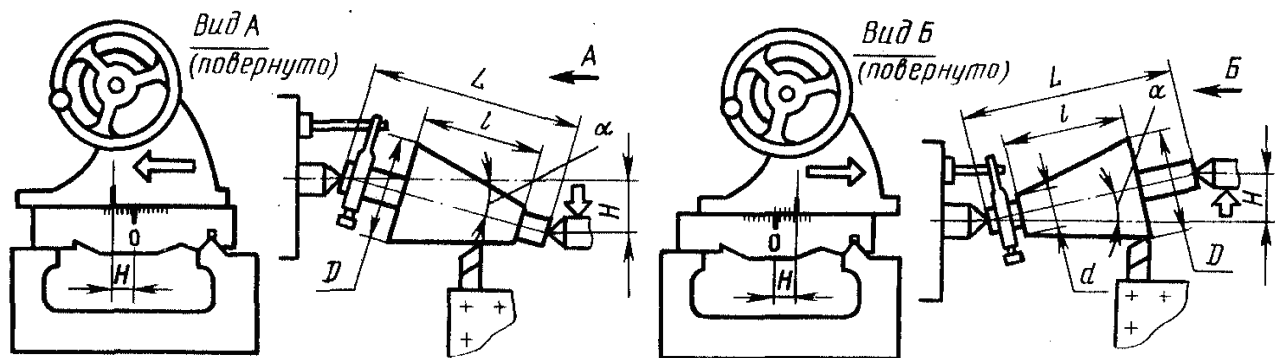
Обработка конических поверхностей способом смещения корпуса задней бабки
